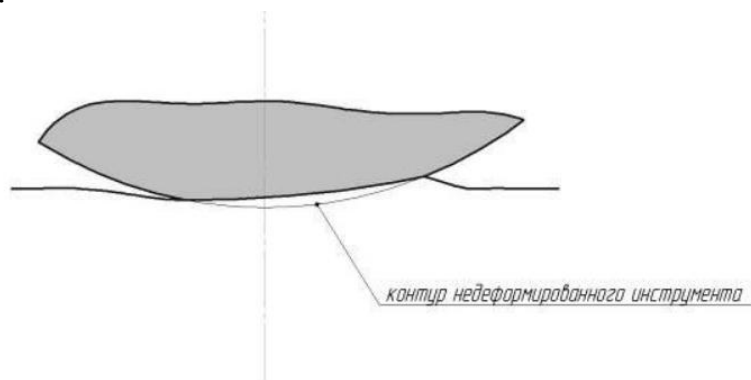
Схема спотворення робочої поверхні інструменту внаслідок його пластичної деформації.
